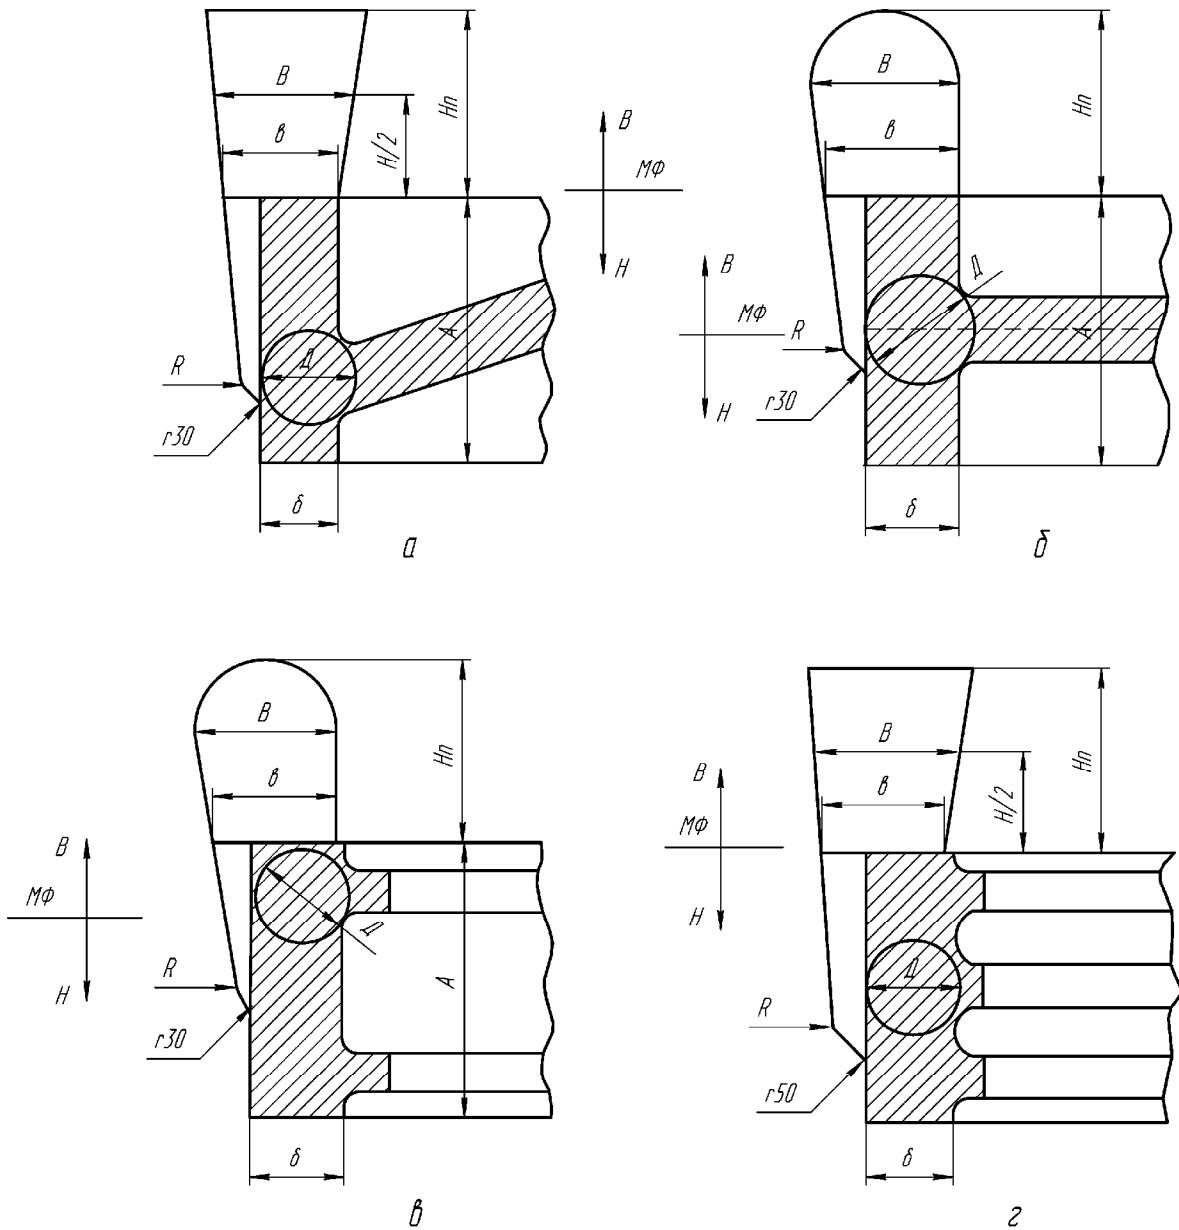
Эскизы прибылей на ободе зубчатых колес:
